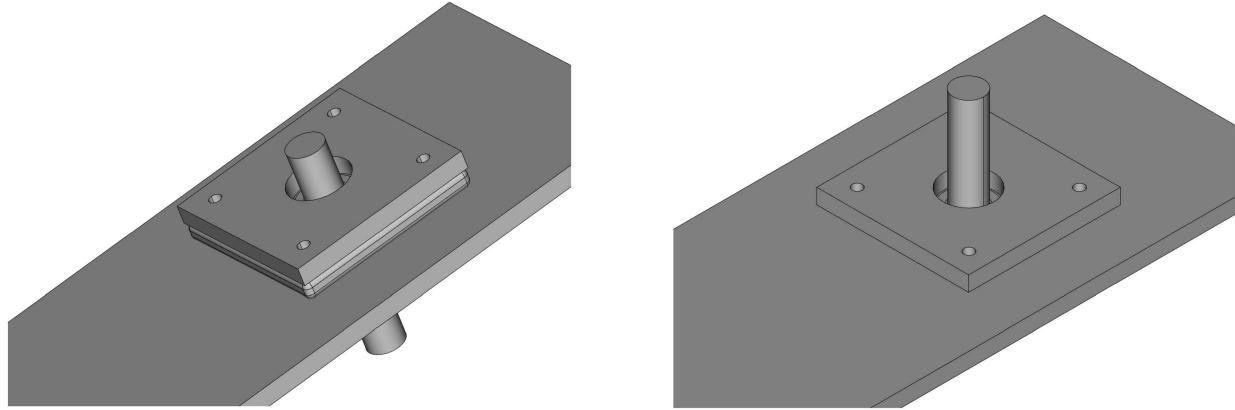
“Rodamiento instalado en barra vertical de soporte lateral; izquierda, vista del lado que tendrá goma (interior); derecha, vista del lado donde se montará engrane (exterior)”.
